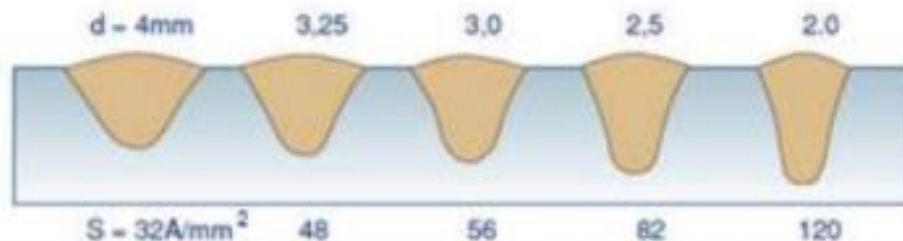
Вплив зміни діаметра дроту на форму зварювального шва
